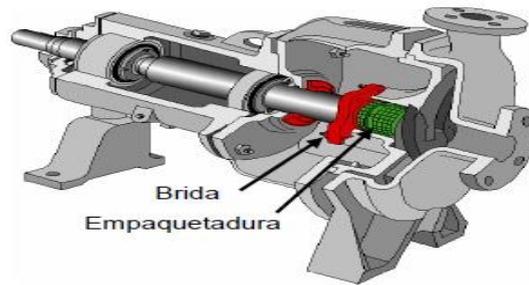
Construcción básica de las empaquetaduras mecánicas
